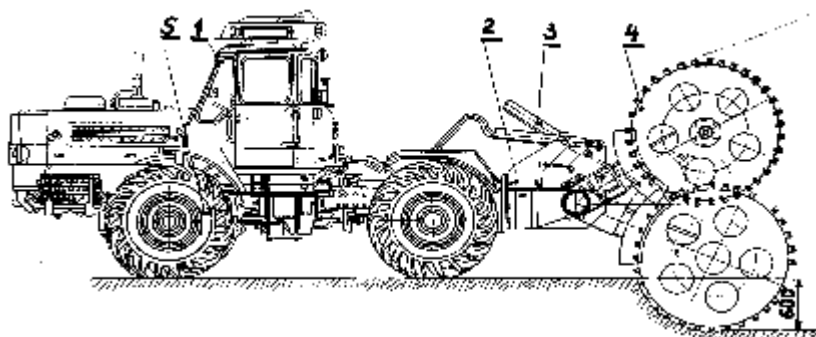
Землерезная машина БТ-150 с диско-фрезерным органом:
